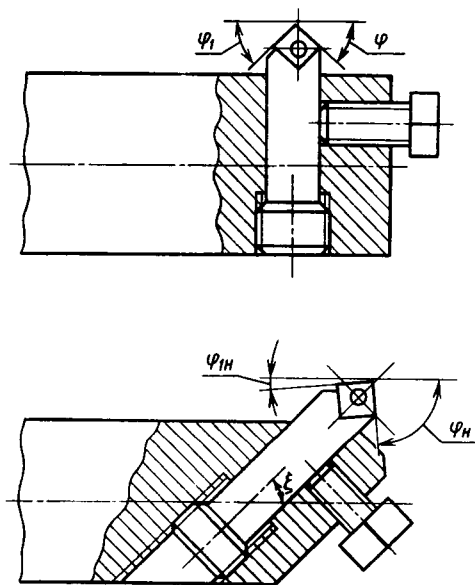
Способы расположения расточных резцов при креплении их в оправках
